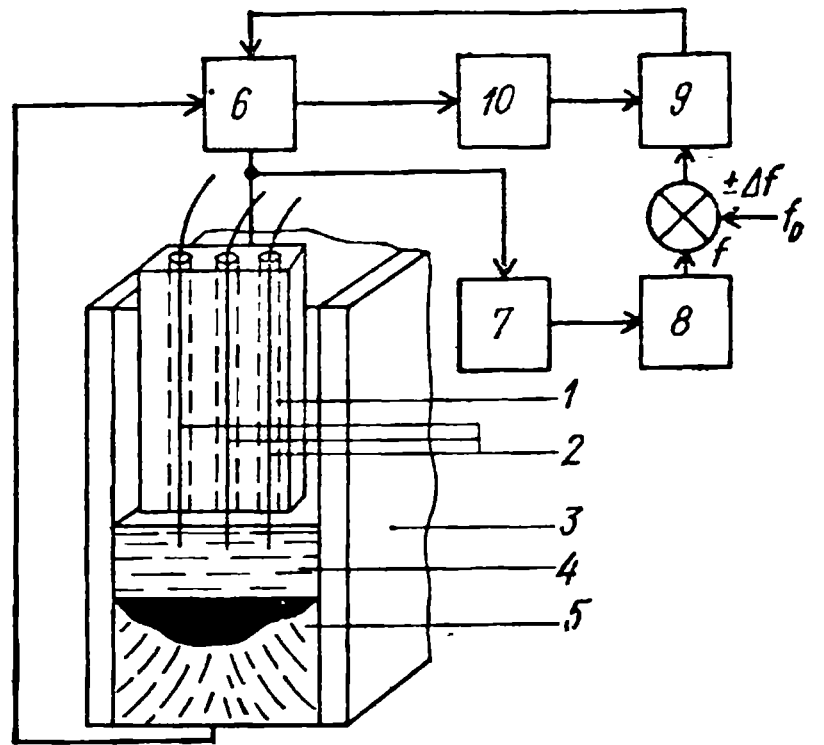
Система регулирования линейной скорости наплавления шва по частоте естественной модуляции сварочного тока
